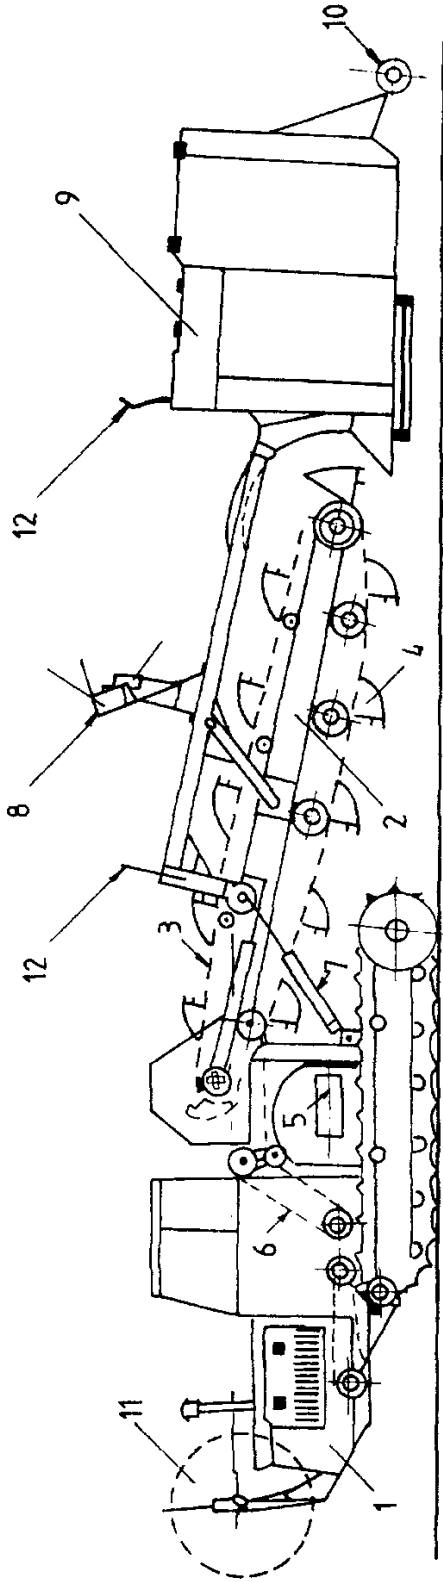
Mașina de drenaj ETT 202 - A cu pozare în tranșee-schema constructivă
